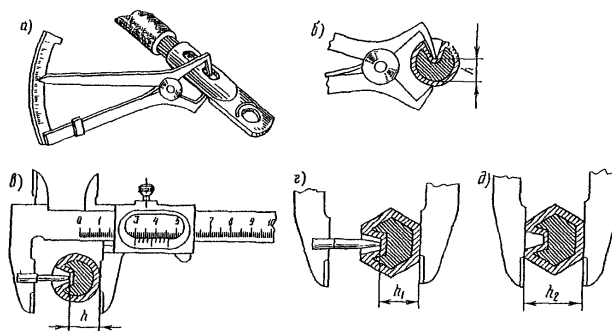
Контроль качества опрессовки: а и б - измерение остаточной толщины при местном вдавливании специальным измерителем; в - то же, штангенциркулем с насадкой; г - измерение остаточной толщины при шестигранном обжатии штангенциркулем с насадкой; д - измерение размеров при шестигранном обжатии штангенциркулем
